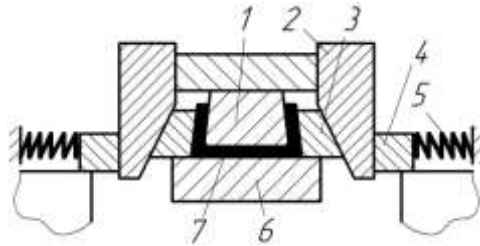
Схема штампа для вигину кутового профілю:
